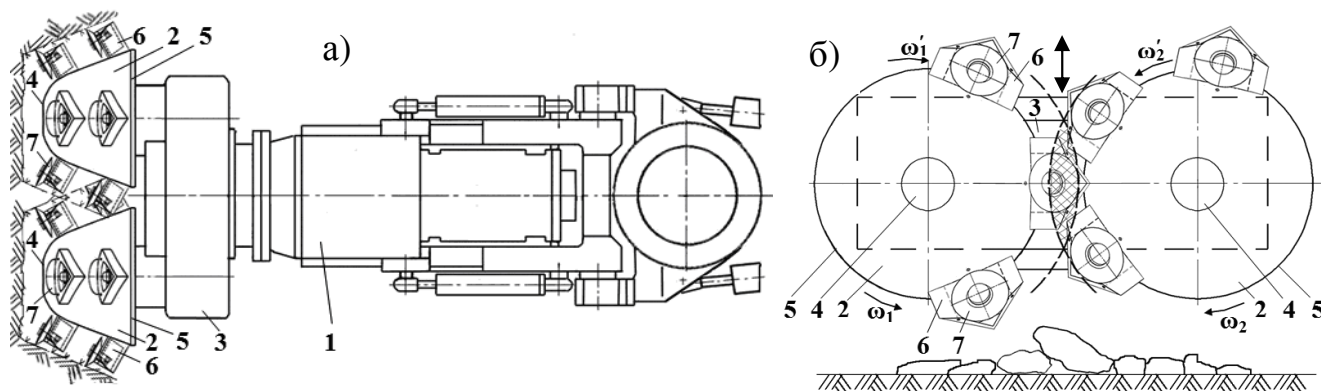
Исполнительный орган с двумя радиальными реверсивными коронами: а) конструктивная схема; б) схема дробления породы; 1 – стрела; 2 – разрушающе-погрузочные коронки; 3 – раздаточный редуктор; 4, 5 – меньшее и большее основание коронок; 6 – трехгранная призма; 7 – дисковый инструмент
